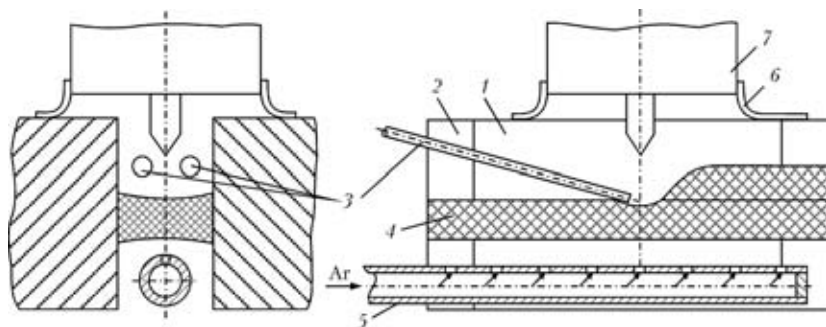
Схема сварки по щелевому зазору: 1 — свариваемая деталь; 2 — выводные планки; 3 — двоянная присадка; 4 — наплавленный металл; 5 — приспособление для поддува; 6 — щиток-отражатель; 7 — сопло горелки
